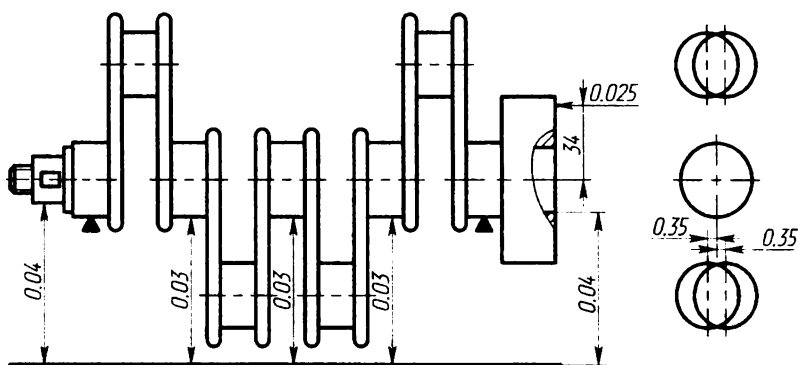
Допустимые биения поверхностей коленчатого вала
